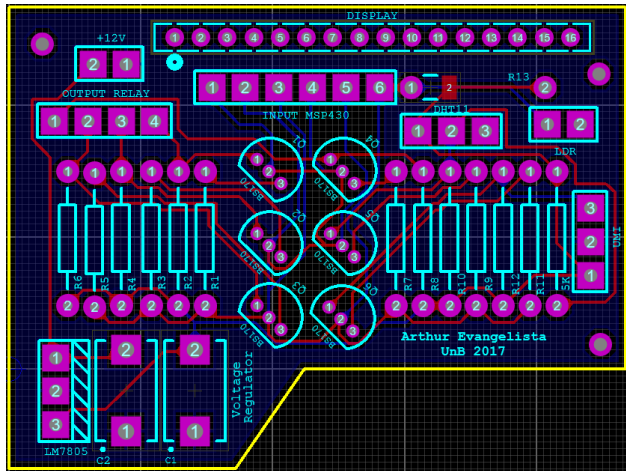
Layout para PCB a ser confeccionada para o projeto.
